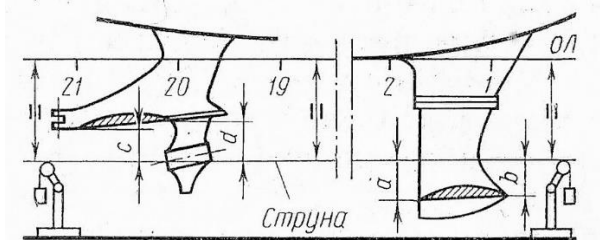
Схема проверки установочного угла крыльев с помощью струн.
